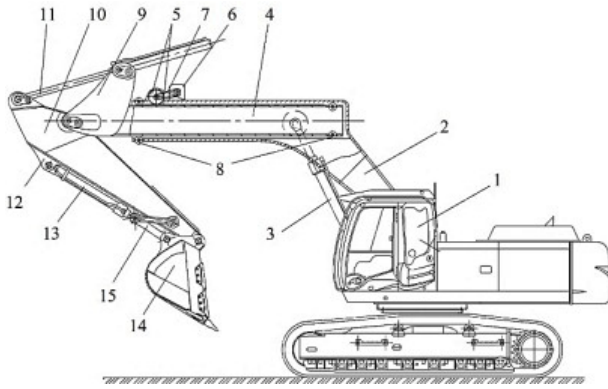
Конструктивна пропозиція патент на корисну модель №75318: 1 – базовий трактор; 2 – телескопічна стріла; 3, 11, 13 – гідроциліндри; 4 – ТС стріли; 5 – зубчато-рейковий механізм; 6 – гідромотор; 7 – клинопасова передача; 8 – роликові опорні елементи; 9 – кронштейн; 10 – рукоять; 11 – гідроциліндр; 12 – кронштейн; 14 – ківі; 15 – чотириланковий механізм
